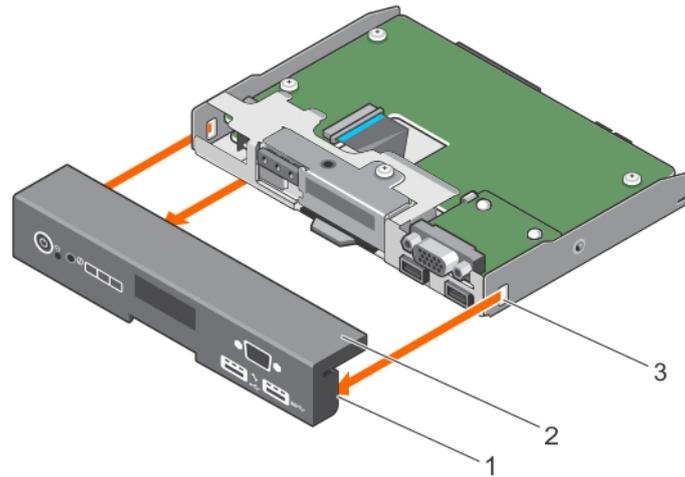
Extracción de la cubierta del ensamblaje del panel de control para un sistema con panel LCD.
